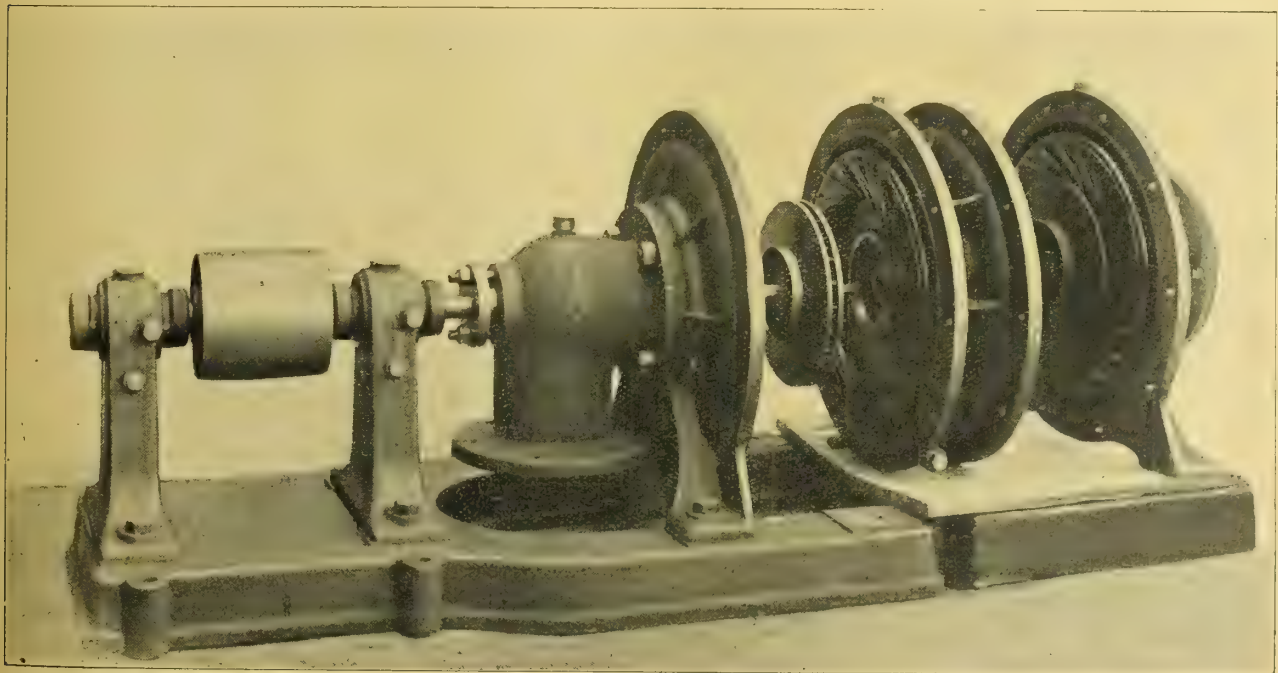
Ansicht einer auseinander genommenen Pumpe, System Jaeger.
